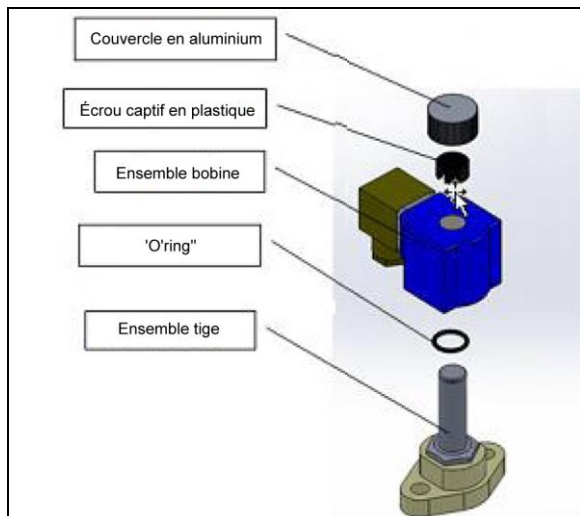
BOBINE DE LA SOUPE DE DÉLESTAGE
